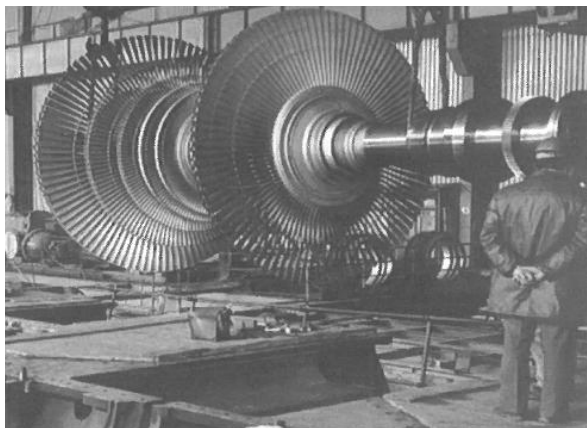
Pierwsza konstrukcja stalowa pierwszego bloku 200MW
